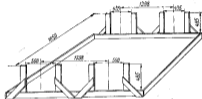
Станок для сборки корпусов катамарана длиной 4 м.
